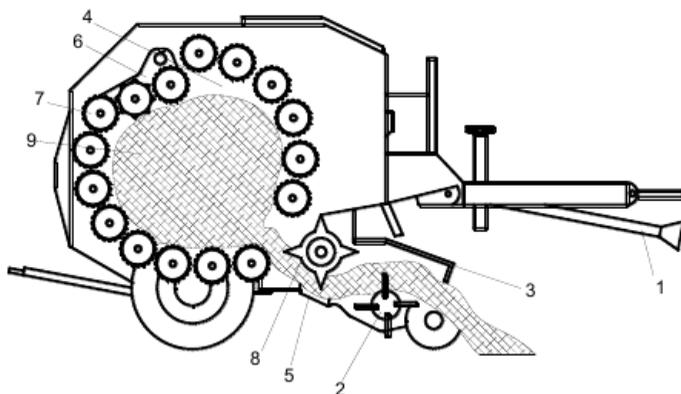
Пресс-подборщик Rollant 250: 1 – карданный вал; 2 – барабанный подборщик; 3 – прижимное устройство; 4 – прессовальная камера; 5 – отражательный щиток; 6 – качающийся сегмент; 7 – прессовальные вальцы; 8 – захватывающий ротор; 9 – прессуемая масса
